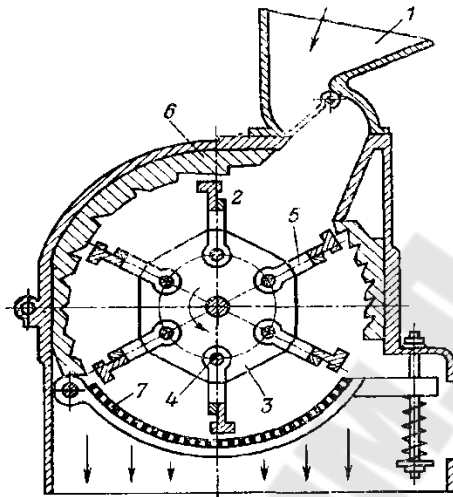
Схема молотковой дробилки: 1- загрузка материала; 2- рабочее пространство; 3- диски; 4- болты; 5- била (молотки); 6- стальная облицовка; 7- решетка
